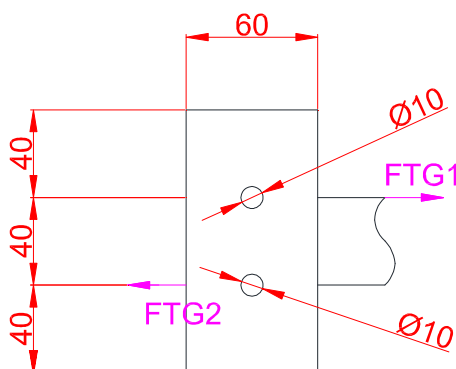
41.- Dimensiones placa lateral brazo elevador
